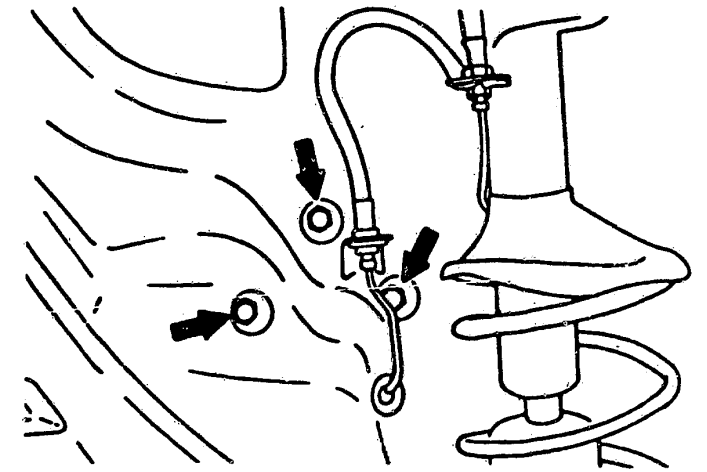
Die Befestigungsschrauben der Getriebeaufhängung sind zugänglich, nachdem die Verschaltung im rechten Radkasten ausgebaut ist.
